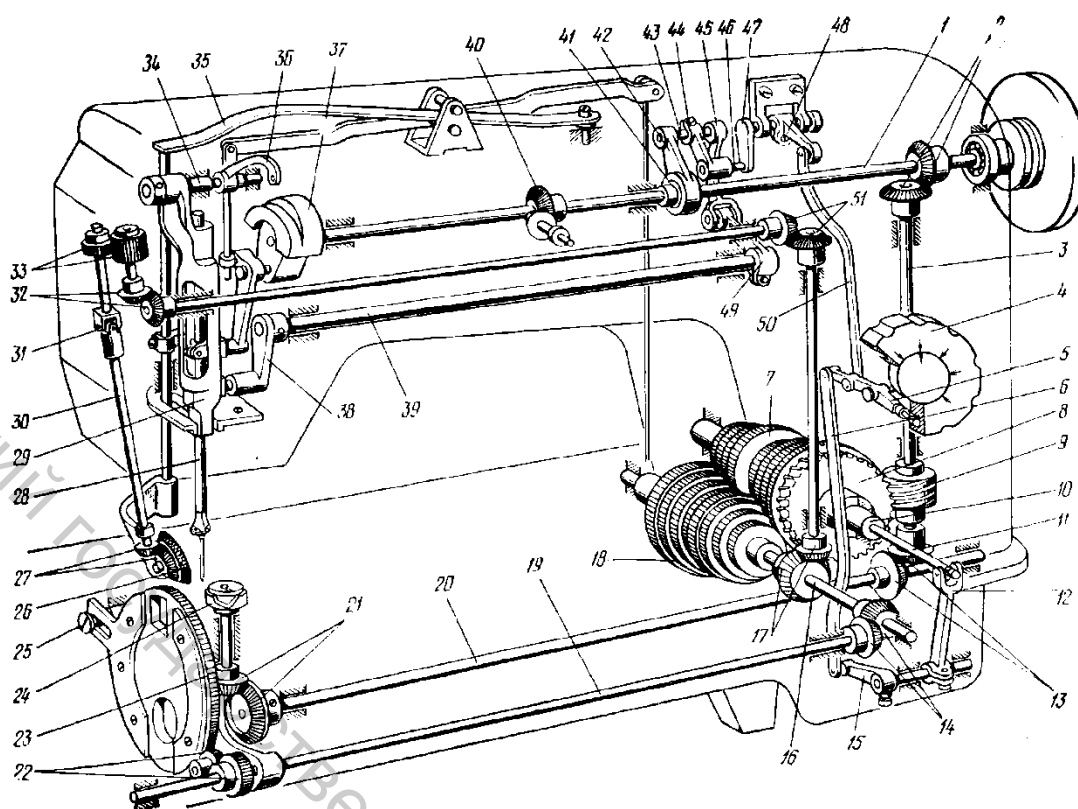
Схема одноигольной челночной швейной машины с плоской платформой
